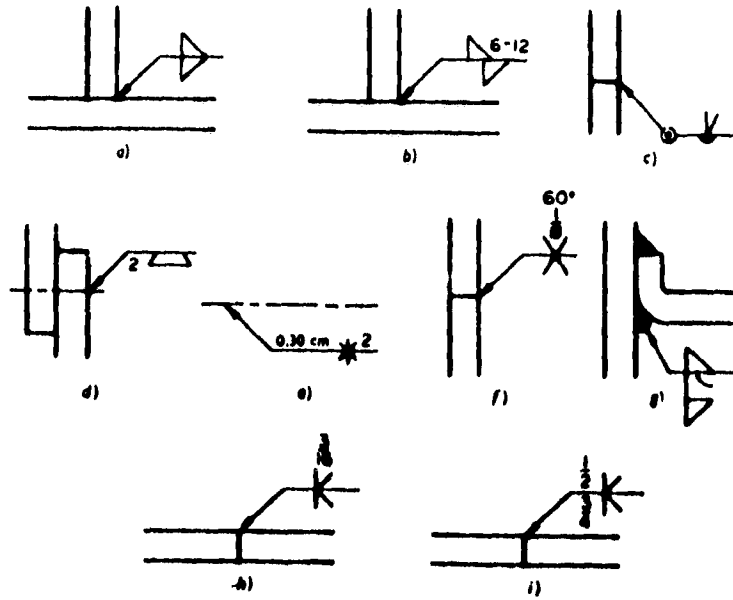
UTILIZACION DE SIMBOLOS PARA PLANOS DE PROYECTOS DE CONSTRUCCIONES SOLDADAS
